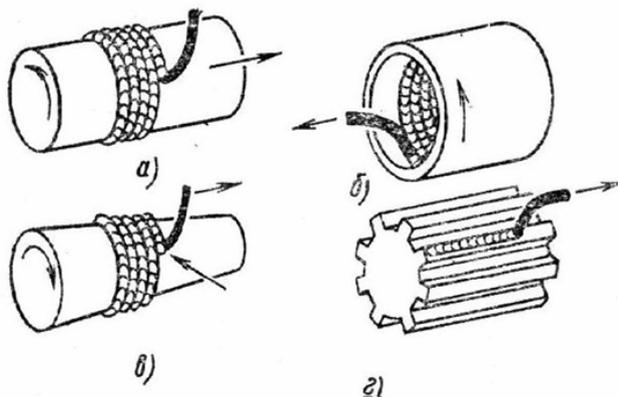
Схемы вибродуговой наплавки изделий различной формы:
